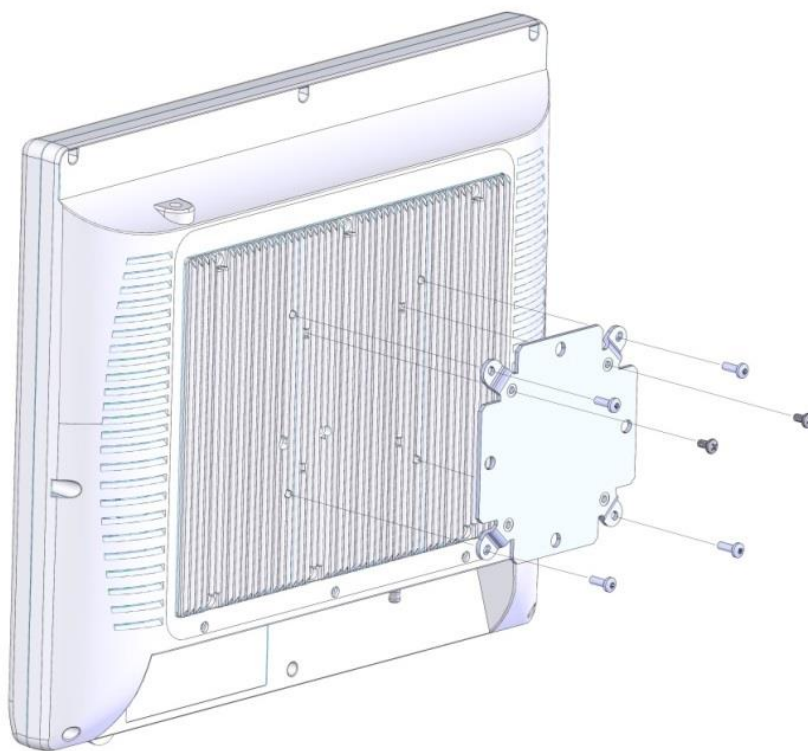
Montar o adaptador de montagem VESA no monitor com tela sensível ao toque
